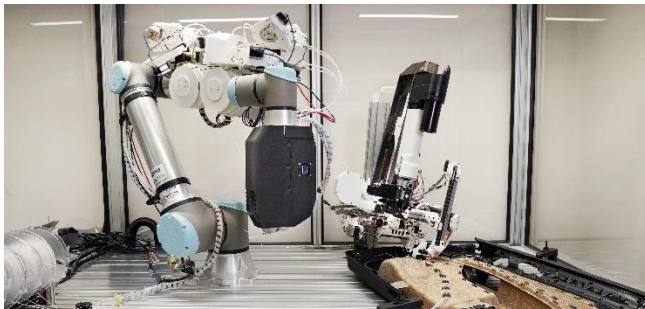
Kabelablage mit AuCA. Das AuCA-System besteht aus zwei Werkzeugen (Kabelablage, links im Bild sowie Kontaktierung, rechts) die an kollaborierenden Robotern geführt werden können. Der Endeffektor »Kabelablage« ermöglicht eine Kabelzuführung von der Endlosrolle, automatische Konfektion, Positionierung und mechanische Anbindung (Thermoplastextrusion) auf dem Bauteil. Es können vier Kabel gleichzeitig verlegt werden. Die Technologie ermöglicht es, flexibel unterschiedliche Kabelbaume vollautomatisch auf dem Werkstück zu fertigen. © Fraunhofer IWU
